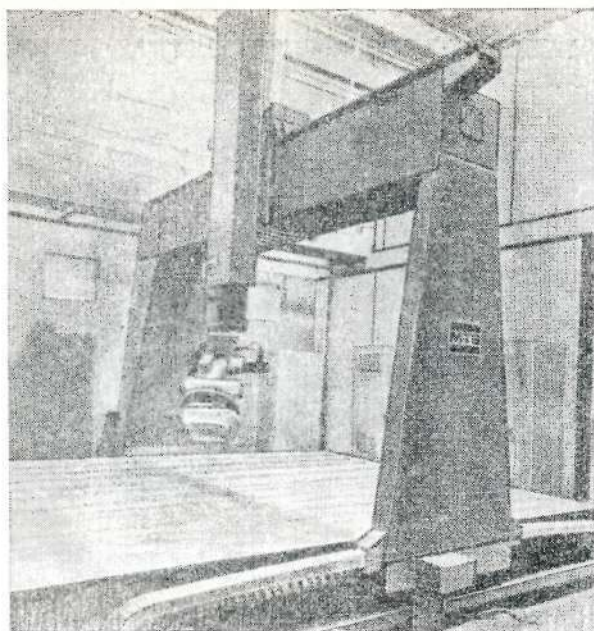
Лазерная система для автоматизации сварочных работ в кораблестроении
